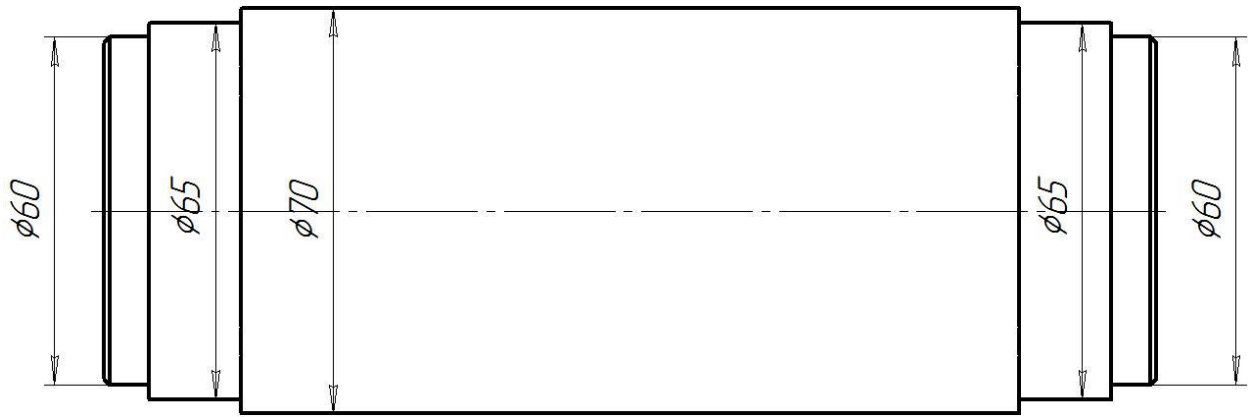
Конструкція п'ятого вала коробки подач
